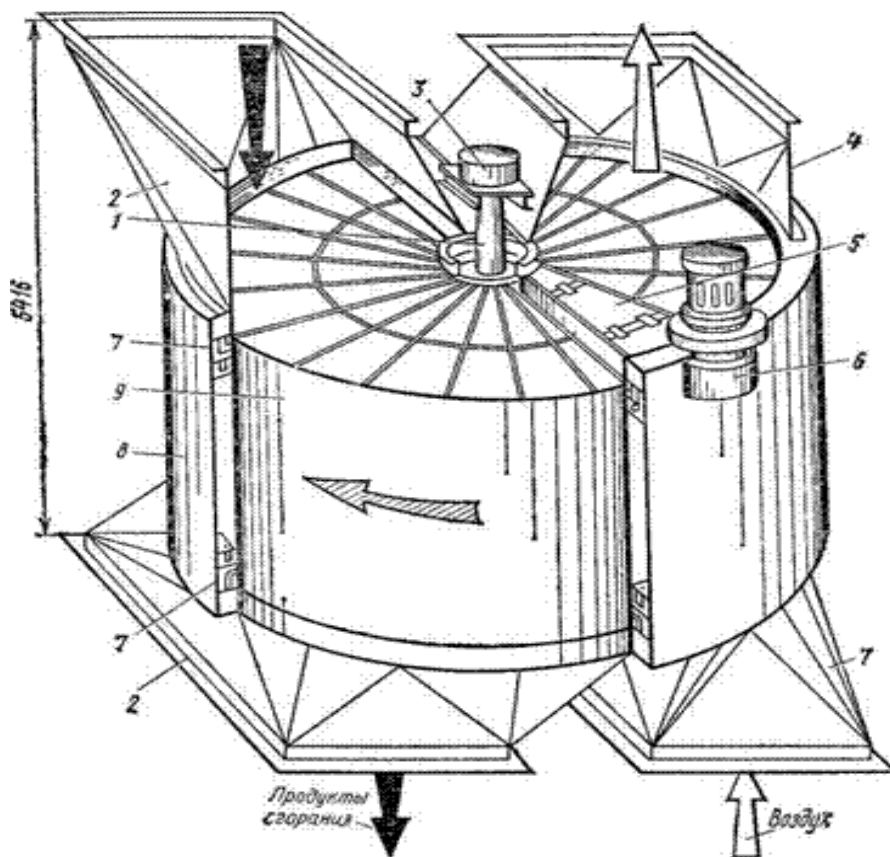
Вращающийся РВП: 1 – вал ротора; 2 – газовые патрубки; 3 – верхний подшипник; 4 – патрубки для воздуха; 5 – радиальное уплотнение ротора, препятствующее перетеканию воздуха в газовый поток; 6 – электродвигатель с редуктором; 7 – наружное уплотнение ротора; 8 – наружный кожух; 9 – ротор
